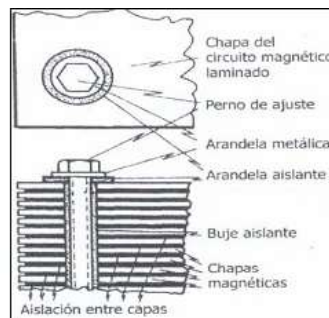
Unión del Conjunto de Chapas Mediante Pernos
